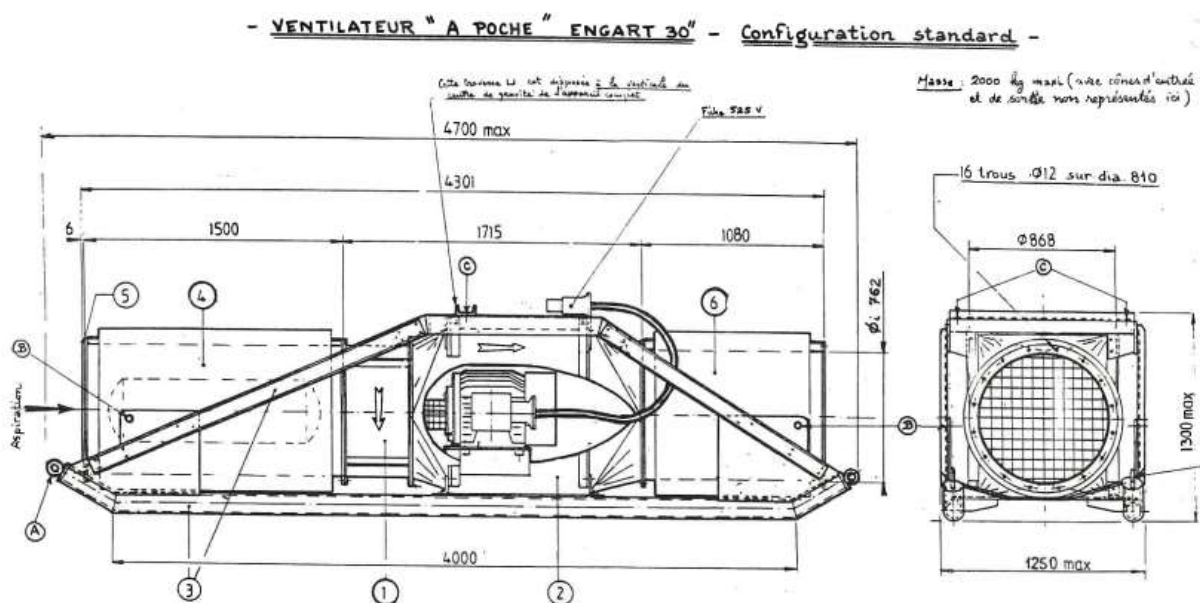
Illustration plan de détail d'un ventilateur ENGART 30"
